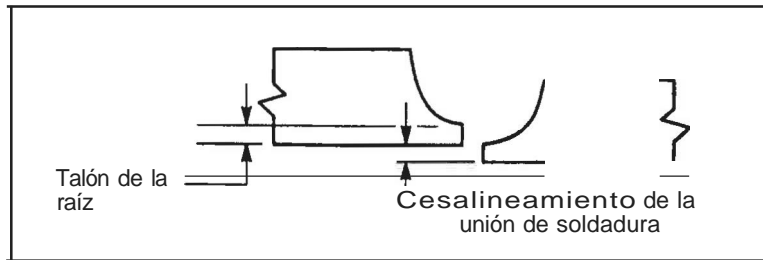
DESALINEAMIENTO DE LA UNIÓN DE SOLDADURA
